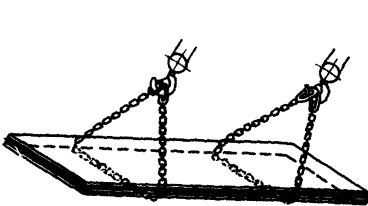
Транспортировка металла и деталей чалочными цепями или стропами из стального каната
